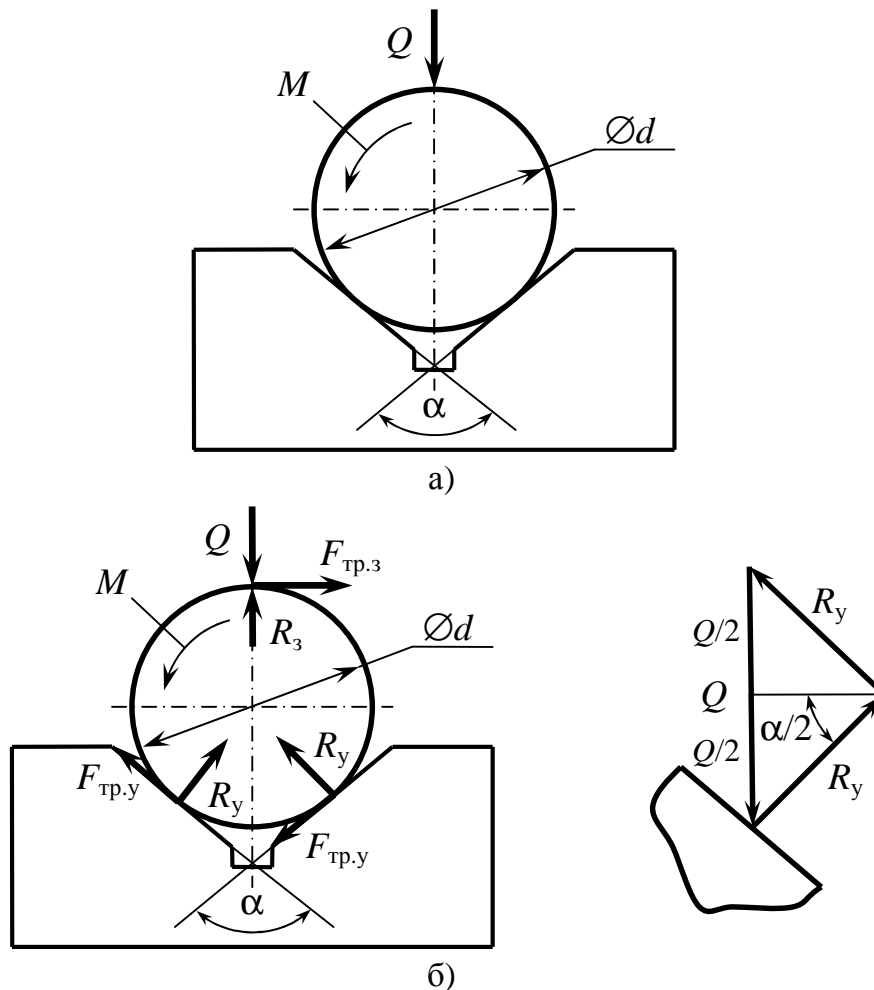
Исходная (а) и расчетная (б) схемы по определению требуемой силы закрепления заготовки при её установке в призму: α – угол призмы; Q – сила закрепления; M – момент сил резания, действующий на заготовку; R_y – реакция установочной поверхности призмы; R_3 – реакция поверхности зажимного элемента; $F_{тр.з}$ – сила трения по зажимному элементу; $F_{тр.у}$ – сила трения по установочному элементу
